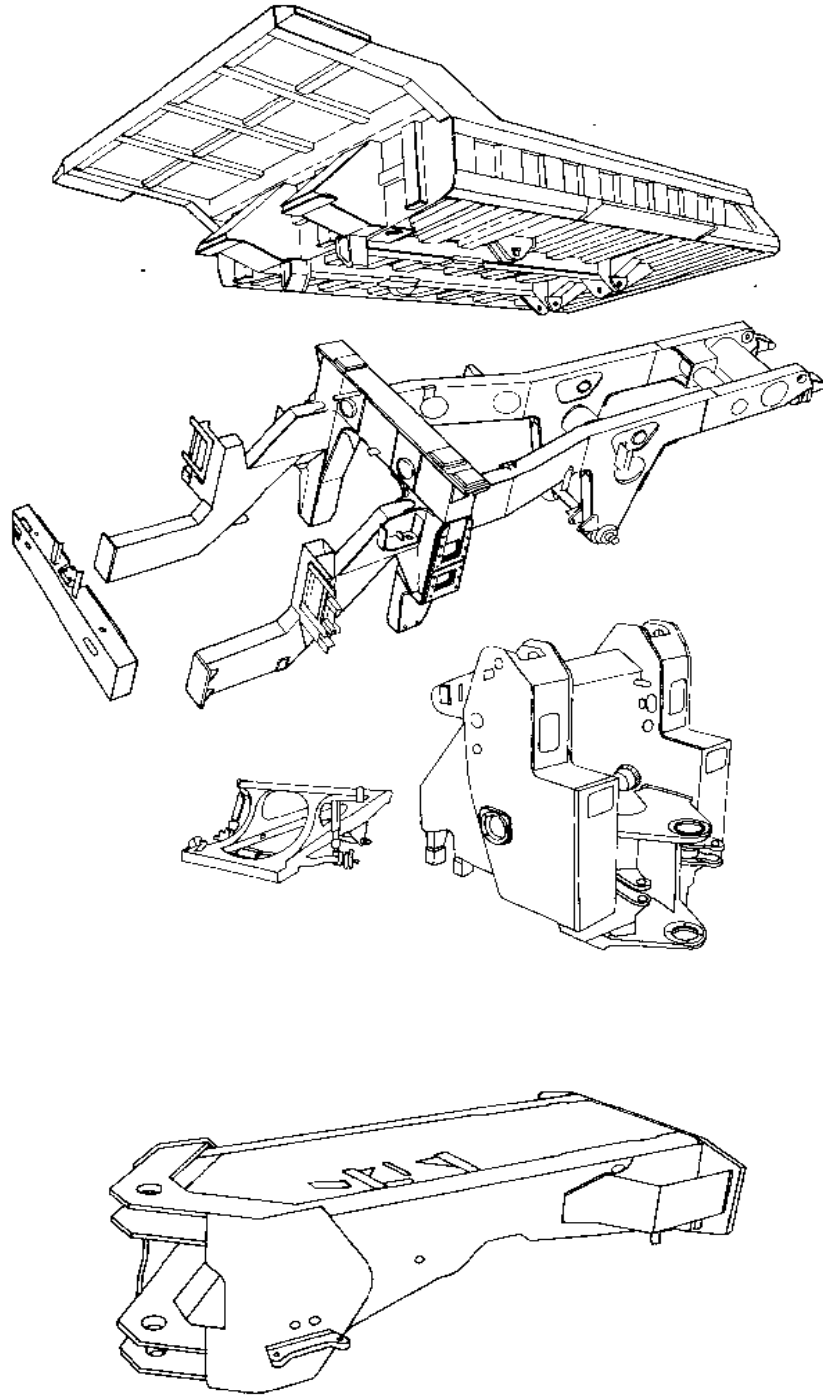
型钢组合梁和钢板焊接梁
